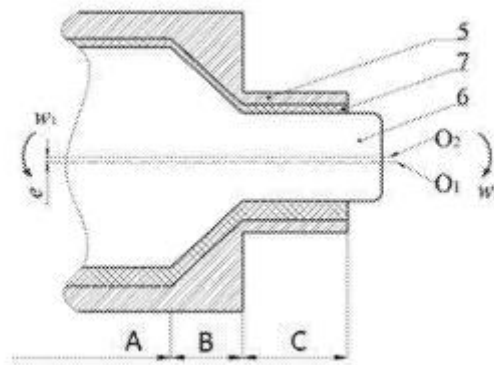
Схема розподілу та формування полімерного розплаву в модернізованій головці екструдера; 5 – внутрішній канал розплаву; 7 – формувальна щілина; 6 – центральний дорн;
